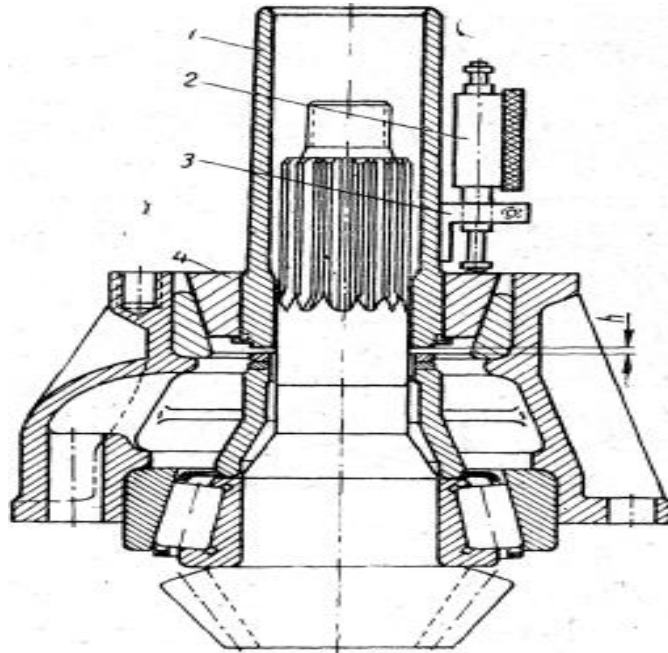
Приспособлення для підбору комплекта регулювальних шайб підшипників вала ведучої конічної шестерні.
